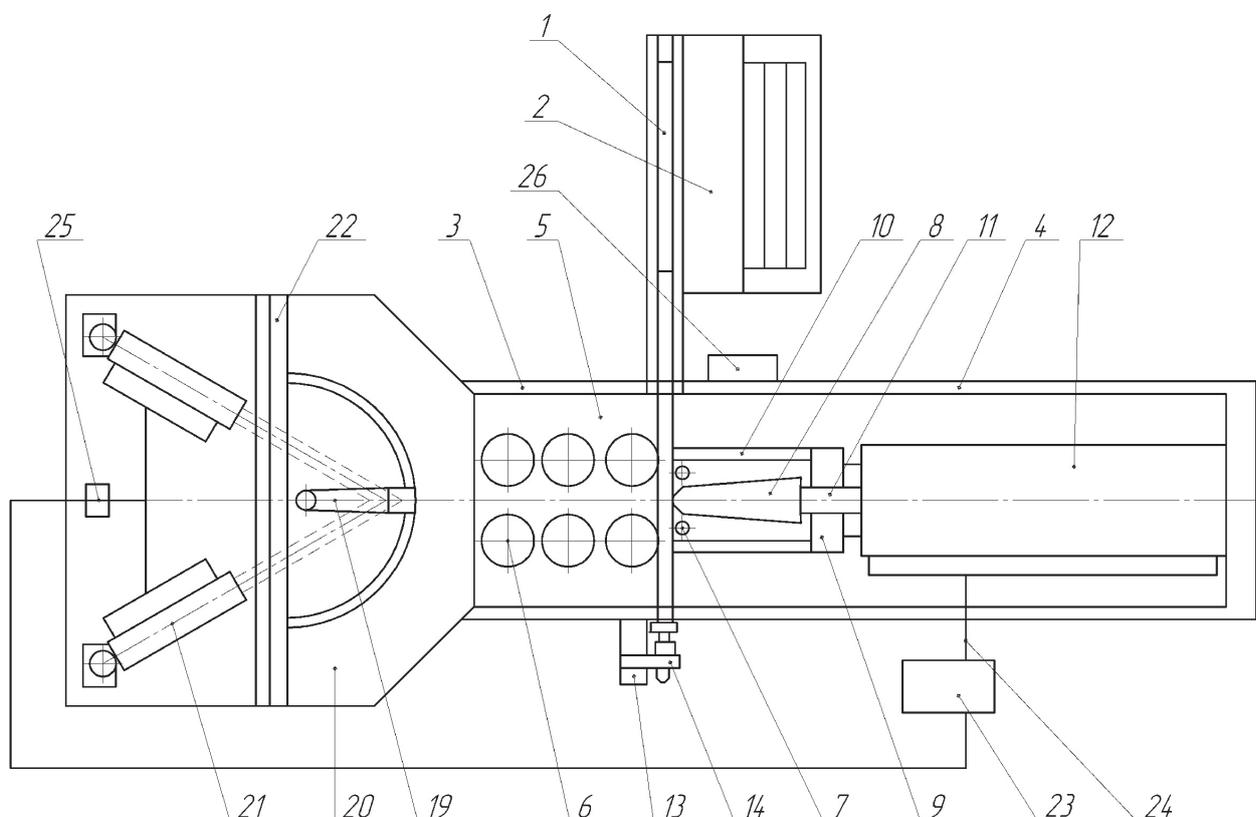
Принципиальная схема стана для прокатки заготовок малолистовых рессор автомобилей МАЗ (вид сверху)
